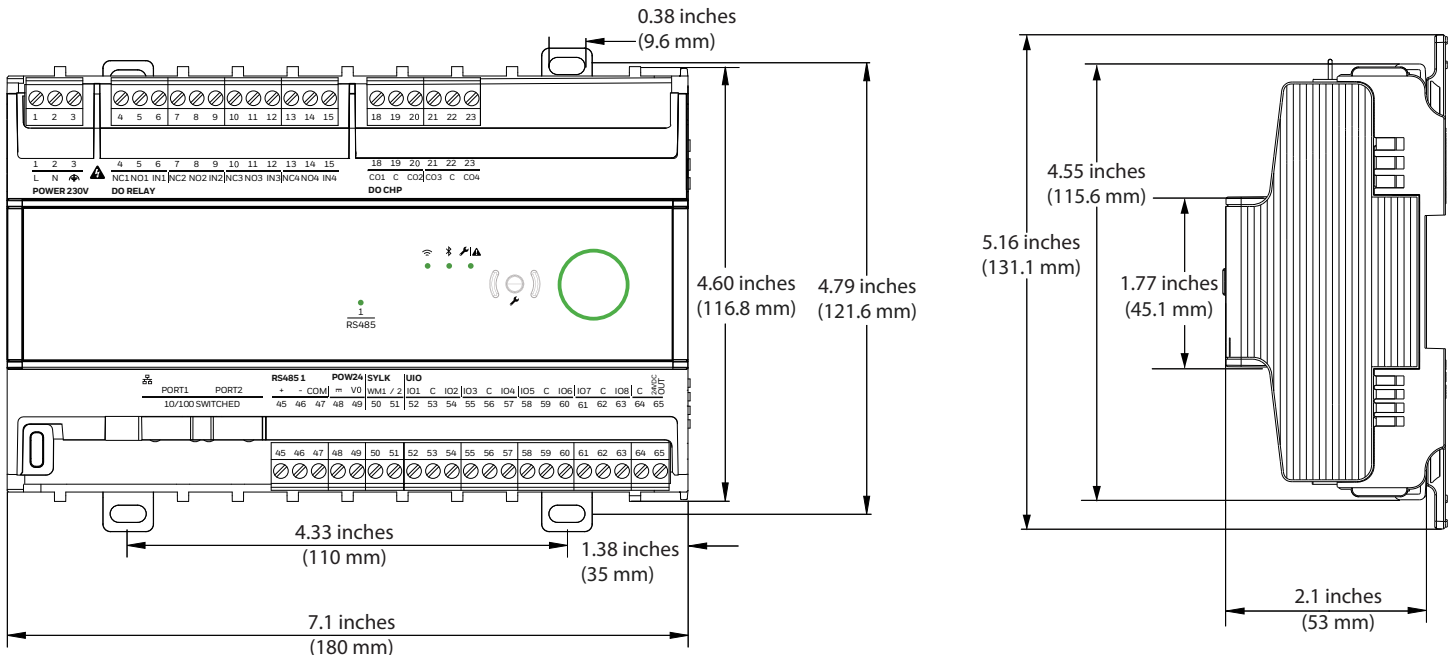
Abmessungen Regler mit kleinem Gehäuse
